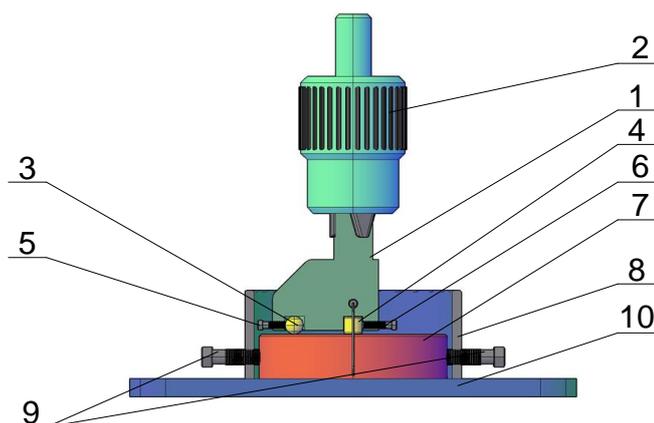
Общий вид экспериментальной установки: 1 – держатель; 2 – патрон; 3 – стальной шарик; 4 – цилиндр; 5, 6 – винты; 7 – основание; 8 – корпус; 9 – винты; 10 – рабочий стол
